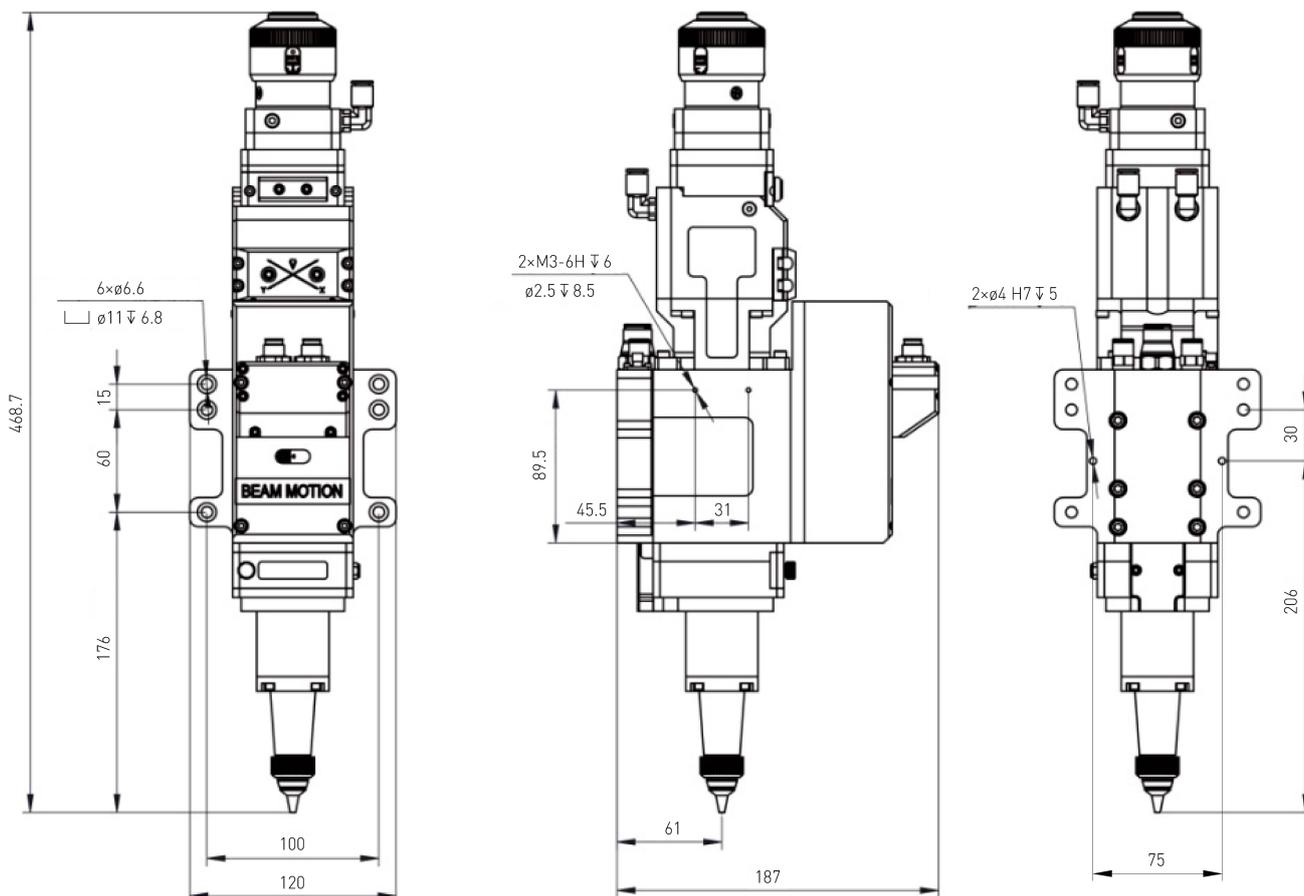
Габаритные размеры и расположение монтажных отверстий.
